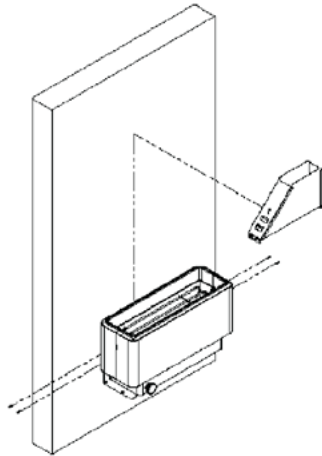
Montage des Abzugssockels am Gerät und Befestigung mit Schrauben
